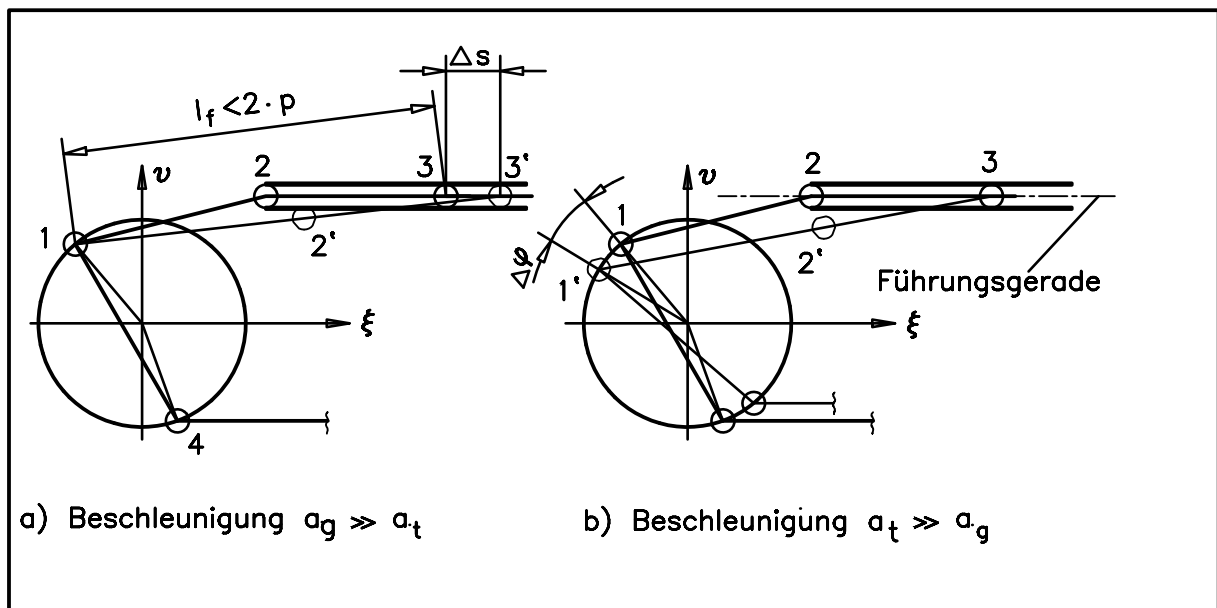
Auslaufwechsel beim Kettentrieb mit Führung
